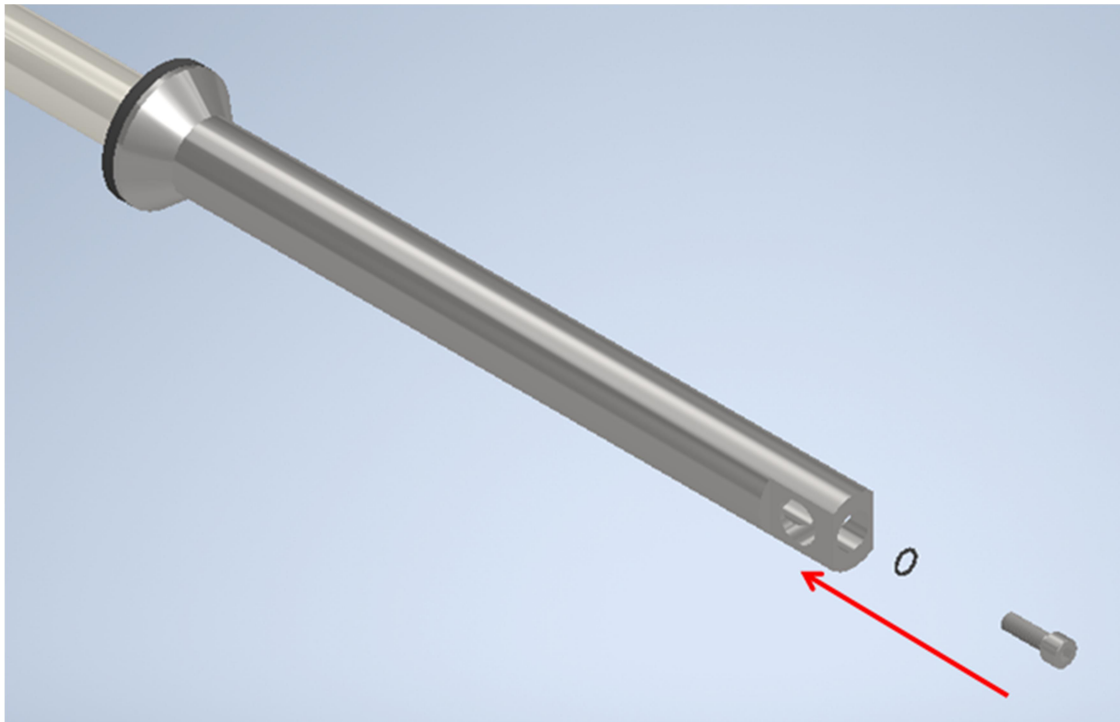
Primeira etapa de montagem com bengala e pistão.
